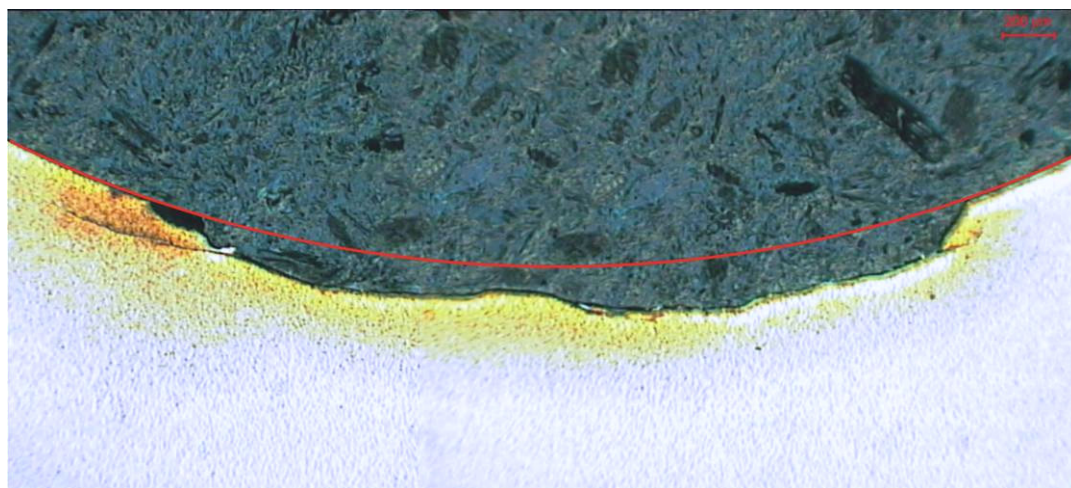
Secção transversal do anel interno do rolamento 1 com indicação do perfil original da pista em vermelho.
